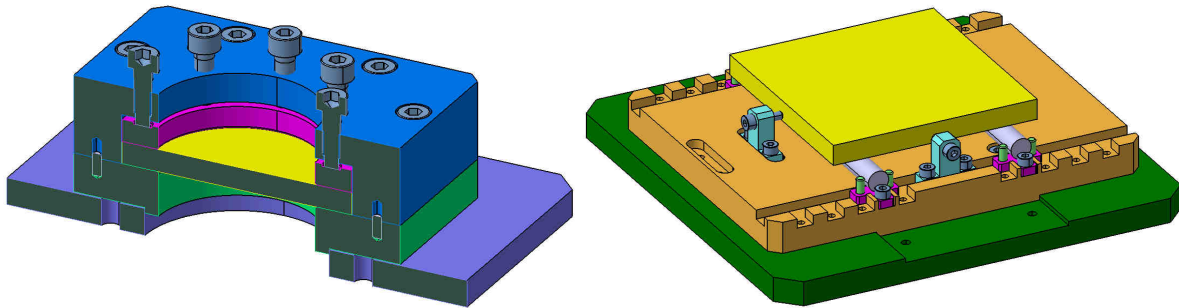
Coupe du montage d'encastrement et montage d'appui simple pour l'essai d'impact par poids tombant
